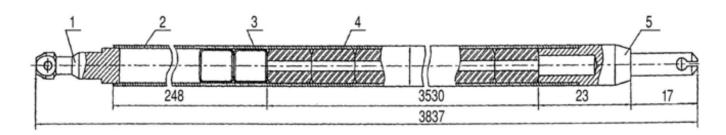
Тепловыделяющий элемент: 1 — заглушка верхняя; 2 — оболочка; 3 — фиксатор; 4 — таблетка; 5 — заглушка нижняя
